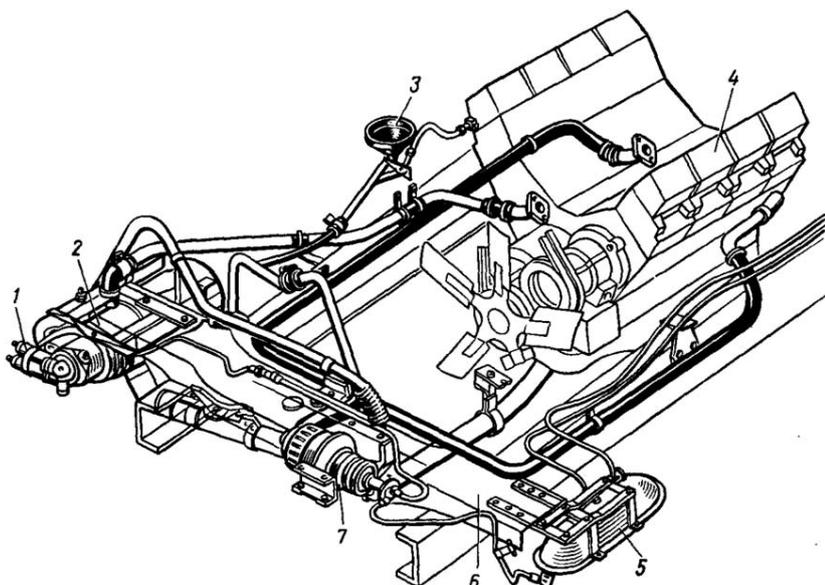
Установка предпускового подогревателя на автомобиле: 1 — электромагнитный клапан; 2 — топливопровод; 3 — котел подогревателя; 3 — воронка для заливки жидкости; 4 — двигатель; 5 — топливный бачок; 6 — передняя поперечина рамы; 7 — насосный агрегат
